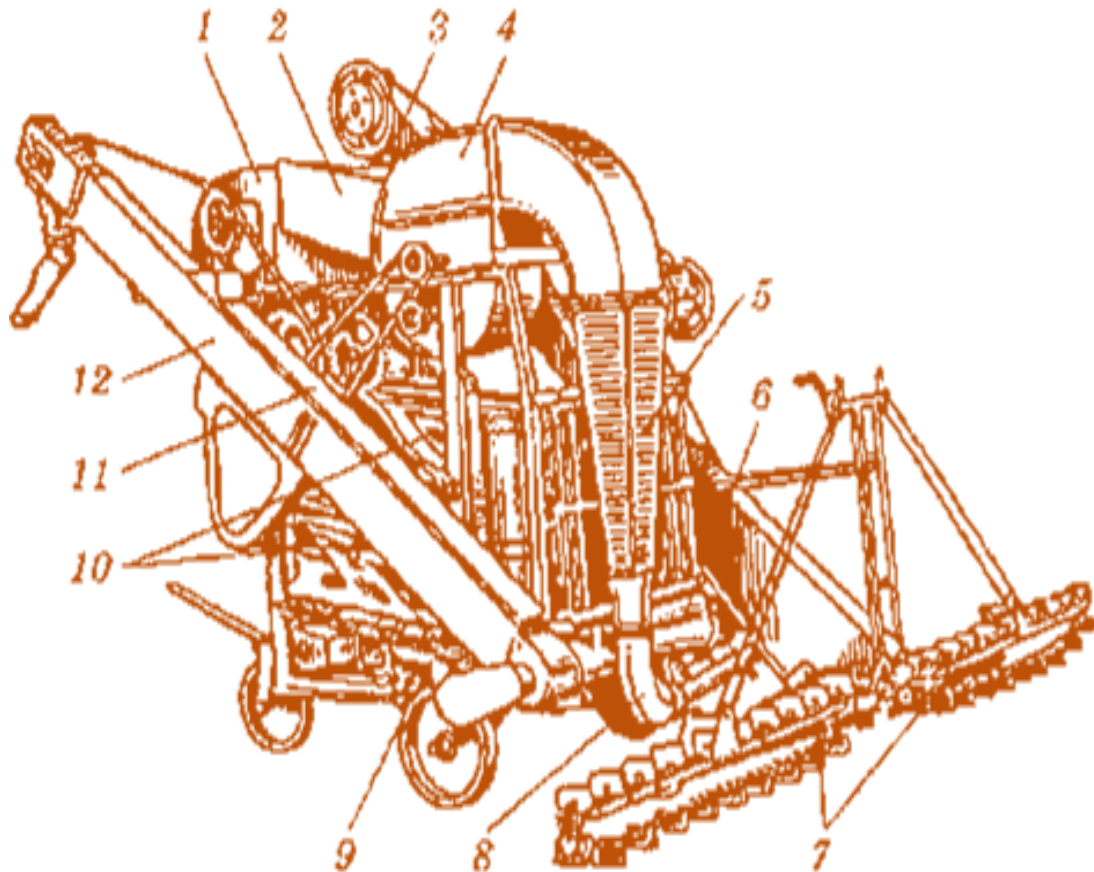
Очисник вороху ОВС-25: 1 - приймальна камера; 2 - корпус повітряної частини; 3 - скребковий конвеєр; 4 - вентилятор шестилопатевий; 5 - інерційний пиловіддільник; 6 - шнек; 7 - скребковий живильник; 8 - пневматичний конвеєр; 9 - механізм самопересування; 10 - решітні стани; 11 - зернозлив; 12 - вивантажувальний конвеєр.
